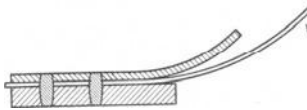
Mit Deckblech durchgeschweißt.
